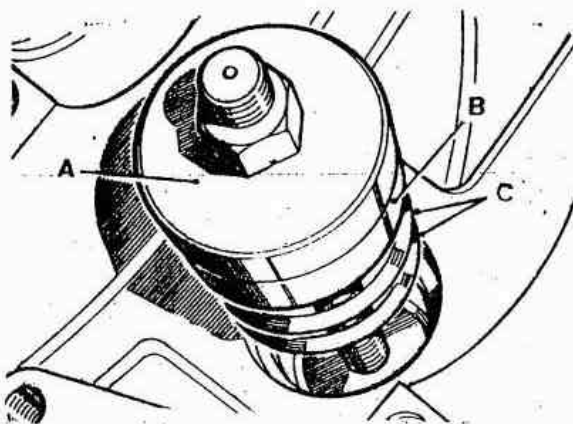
Arandelas-suplemento y montaje de la pista del cojinete de cabeza
